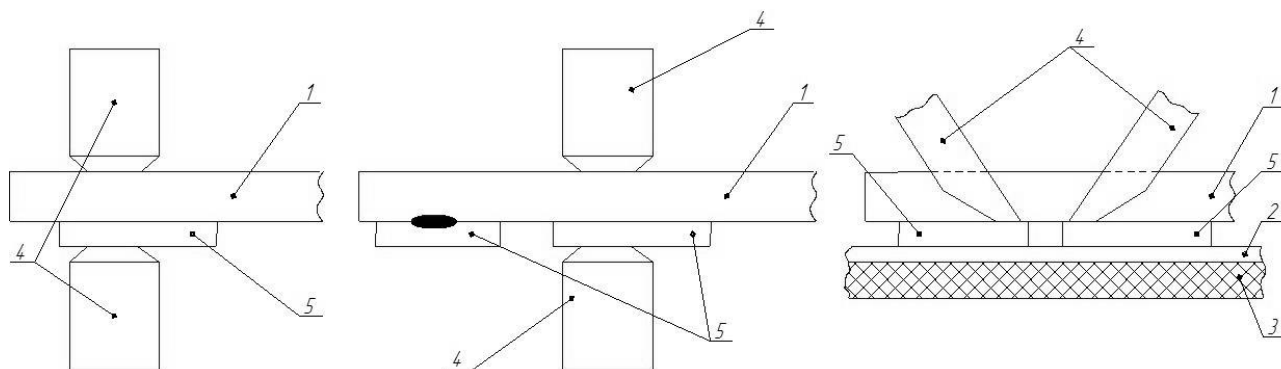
Схема сварки провода через две контактные площадки: 1 – провод, 2 – фольга, 3 – полиимидная подложка, 4 – электроды, 5 – контактная площадка.
